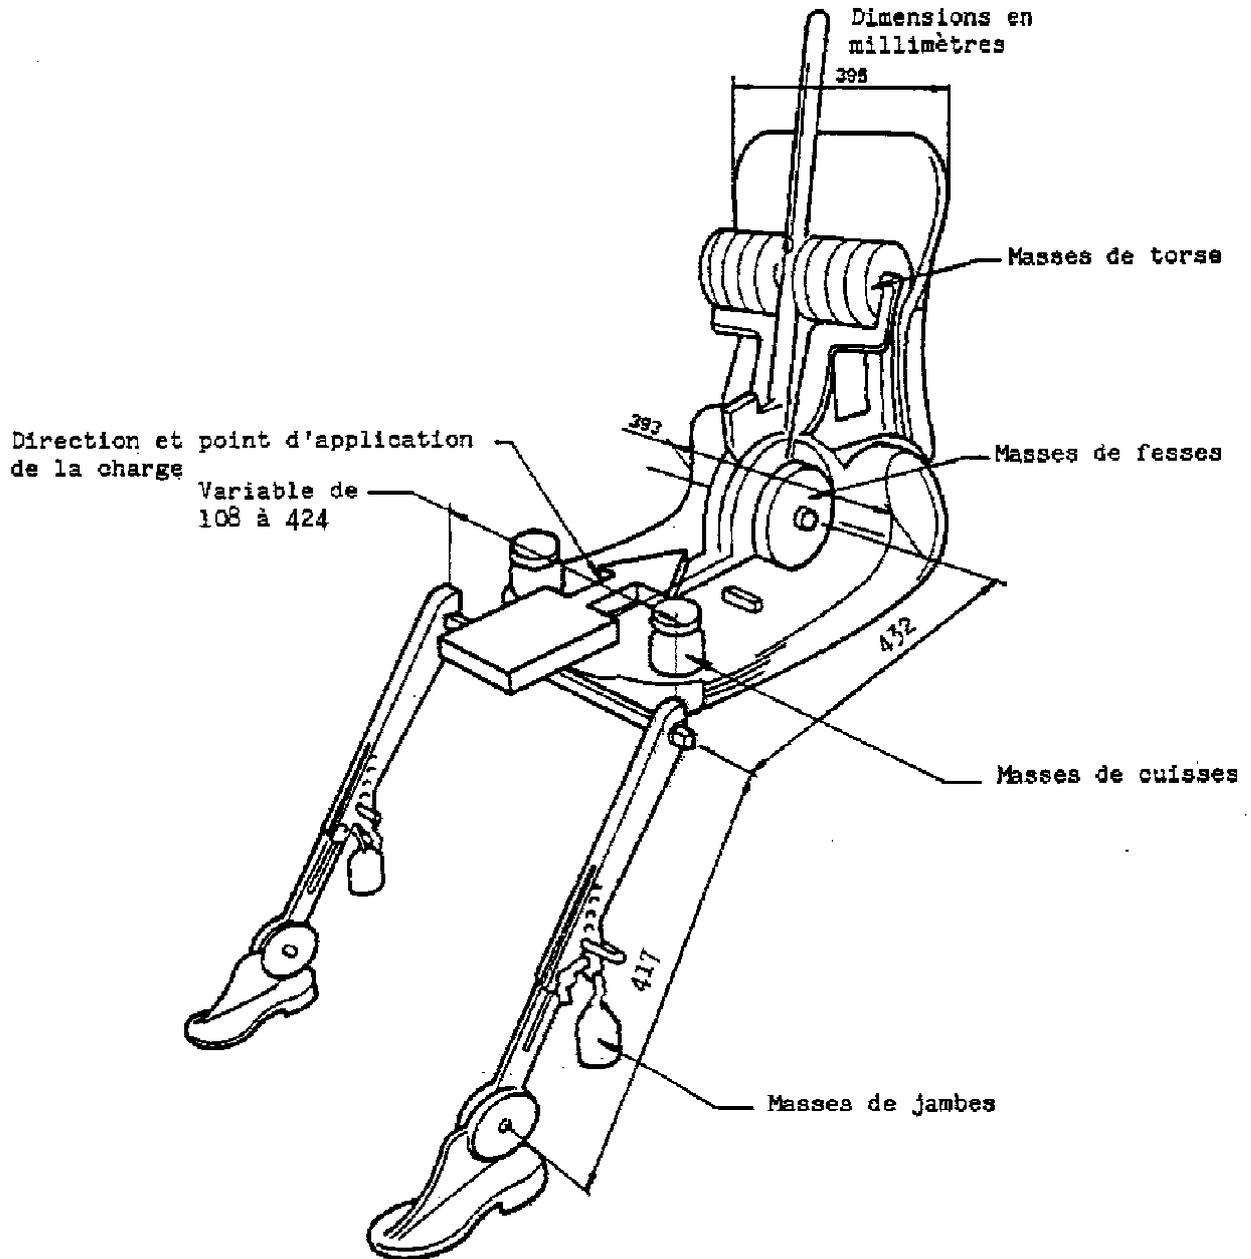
Dimensions des éléments de la machine 3-D H et emplacement des masses
